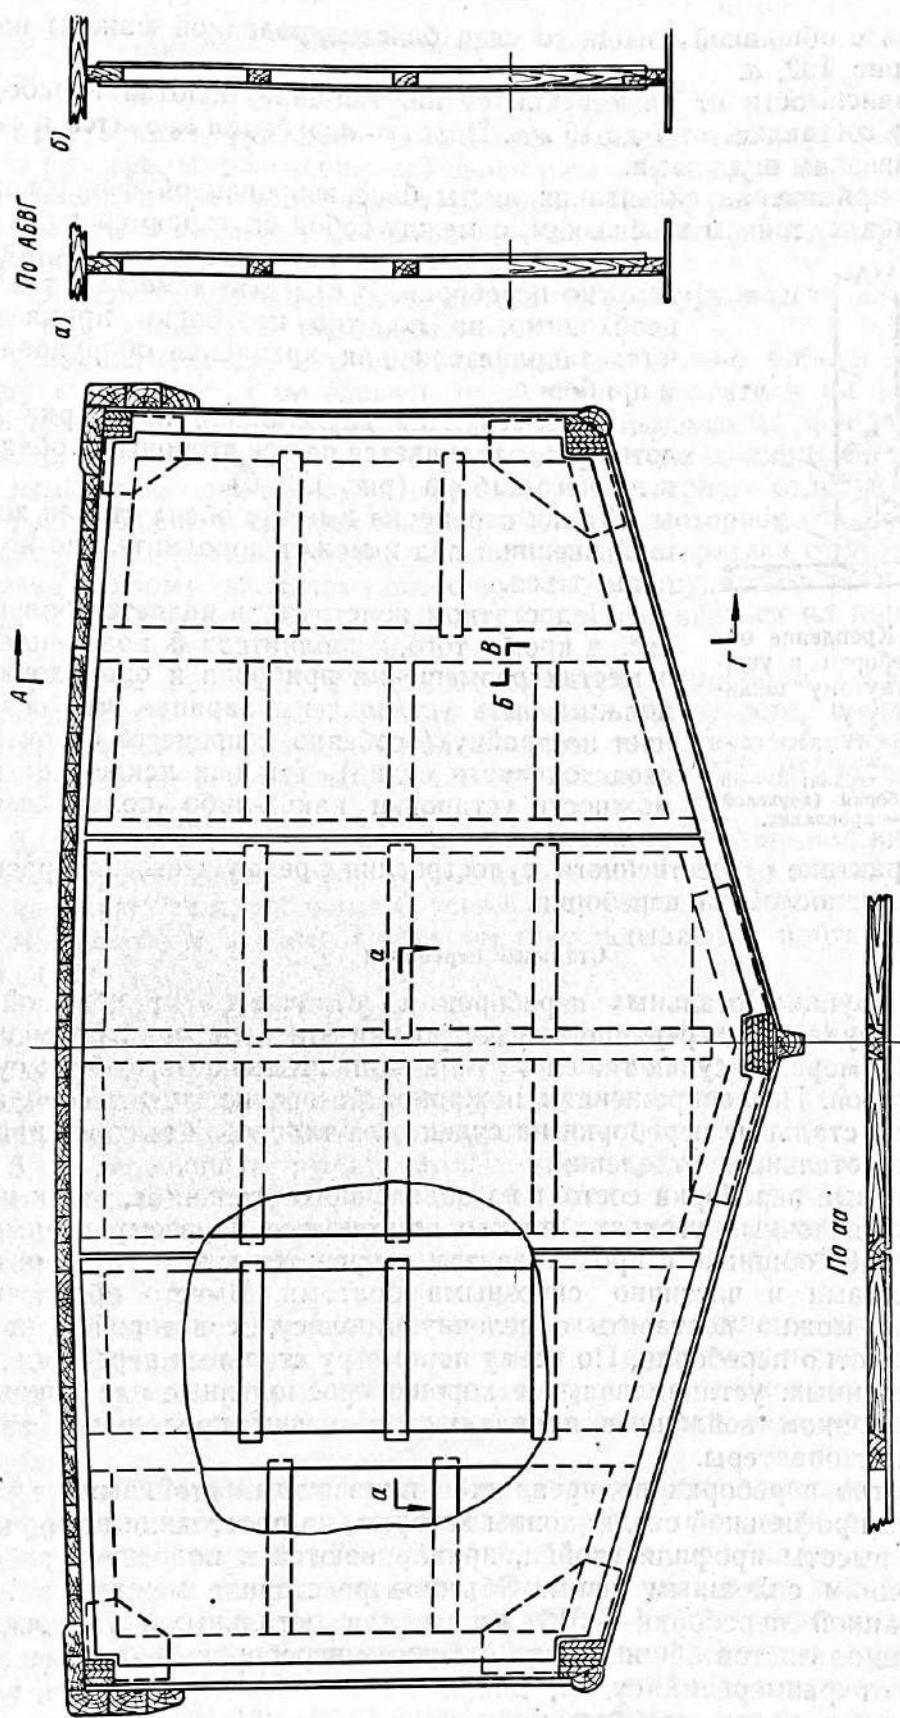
Поперечная переборка с обшивкой из бакелитированной фанеры: а — однослоиня обшивка; б — двухслойная обшивка.
